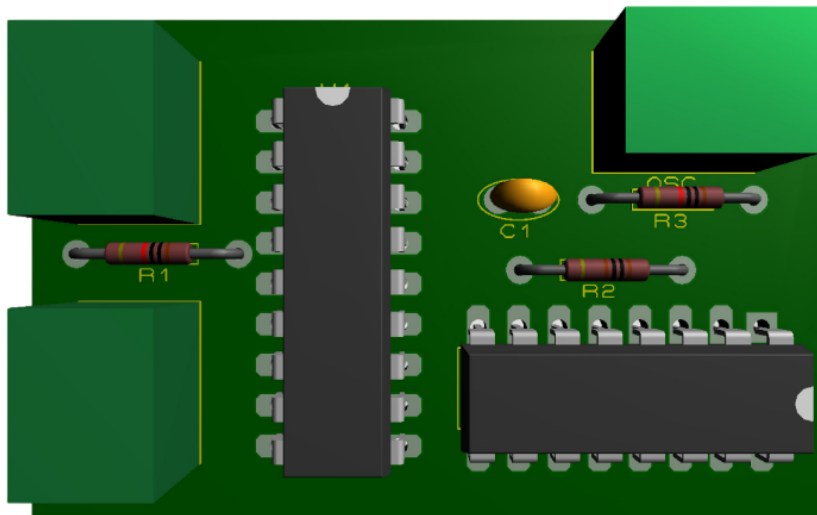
Diseño 3D de la placa PCB. Autor propio.
